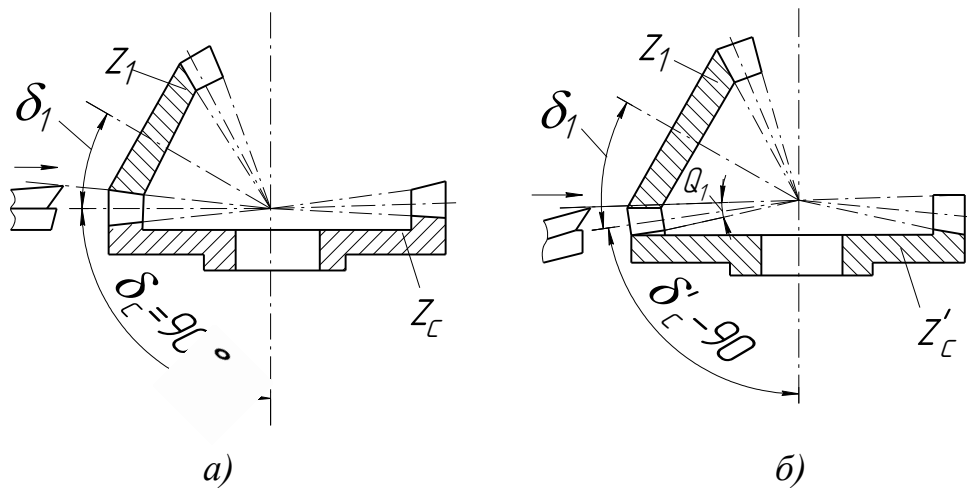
Схеми зачеплення заготовки з плоскими твірними колесами
